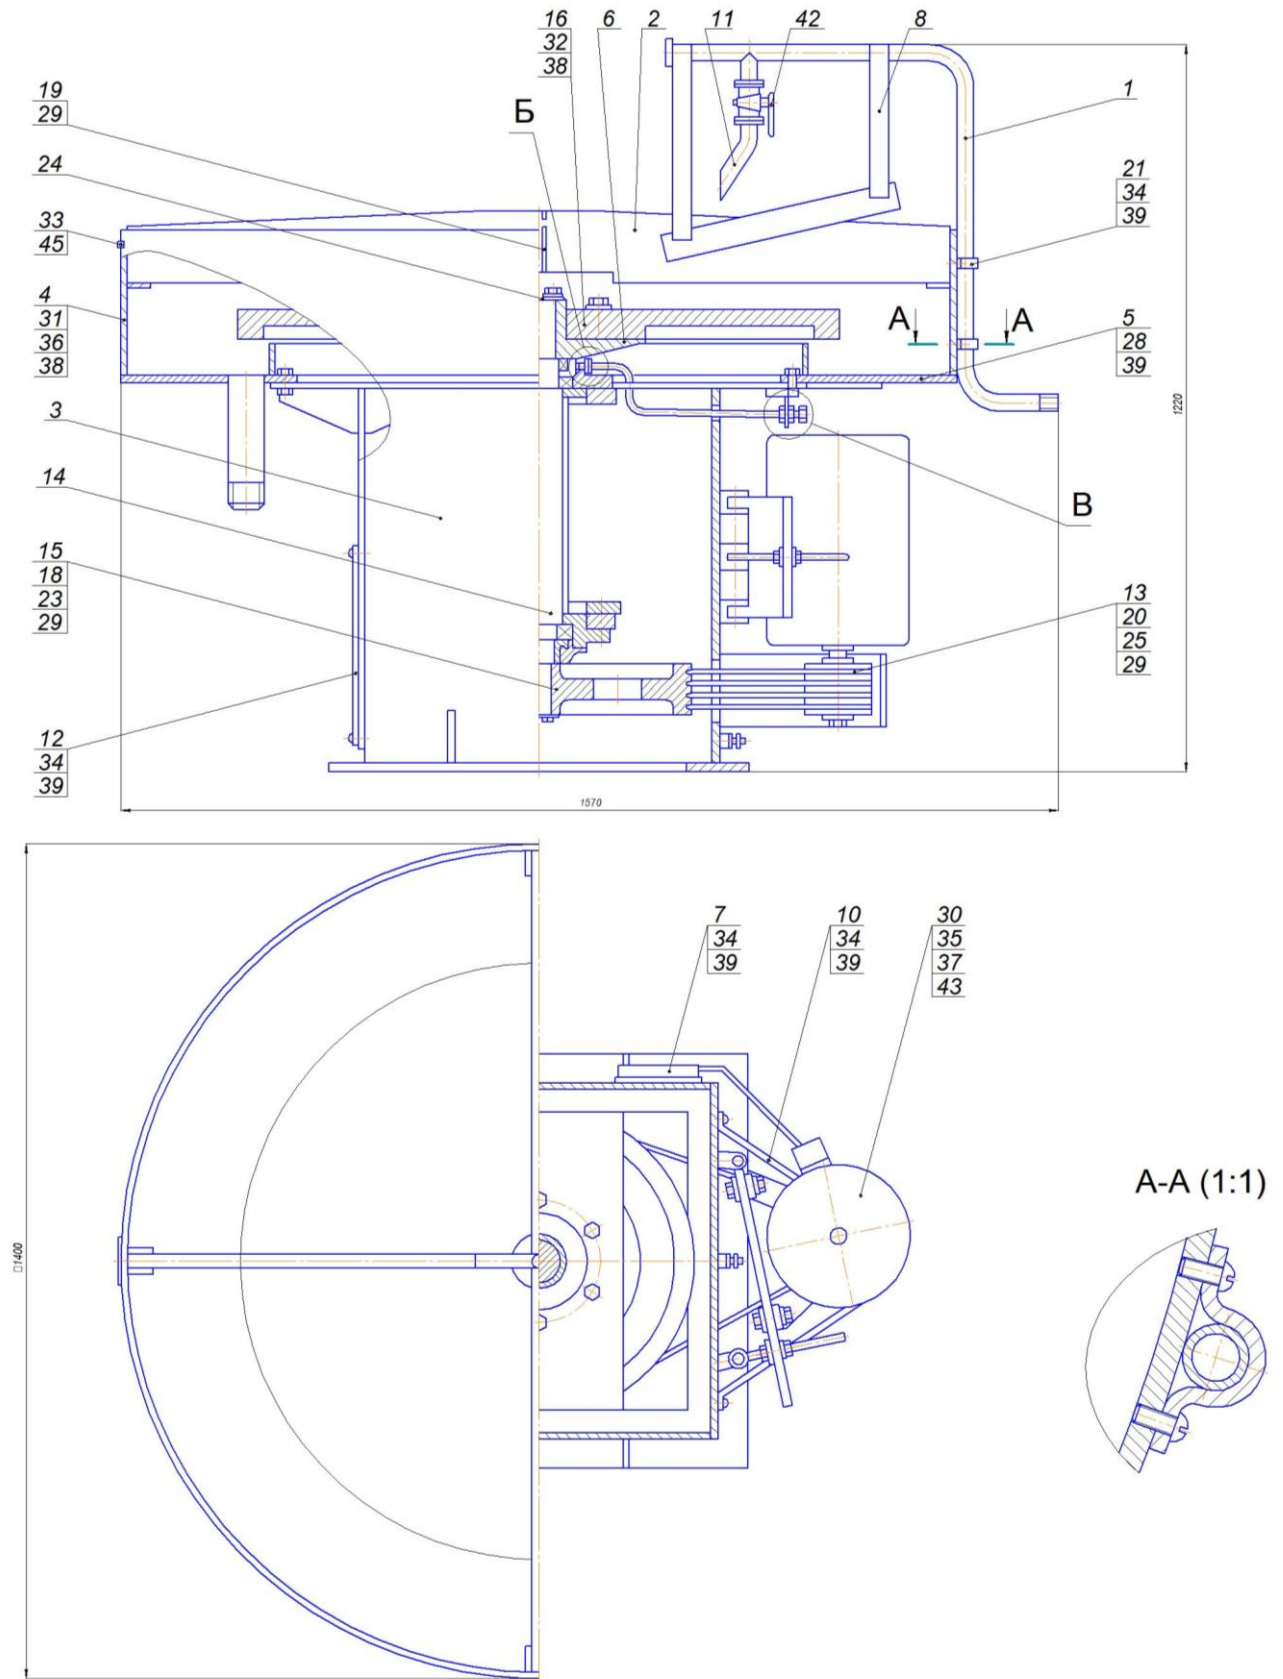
Базовий варіант верстату для шліфування плиткового скла
